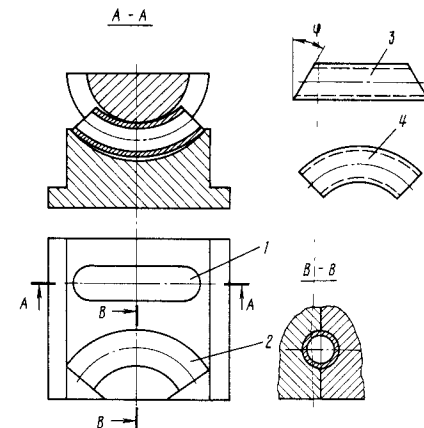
Схема штампа для гибки короткой трубы: 1 — гибочный ручей; 2 — калибровочный ручей; 3 — заготовка; 4 — деталь
